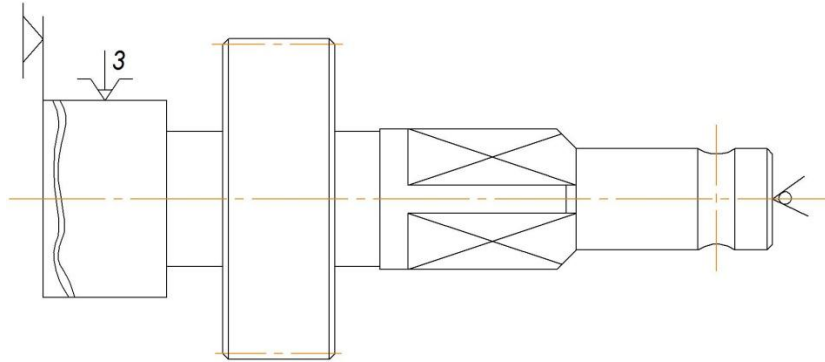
Ескіз обробки деталі на 045 операції.
